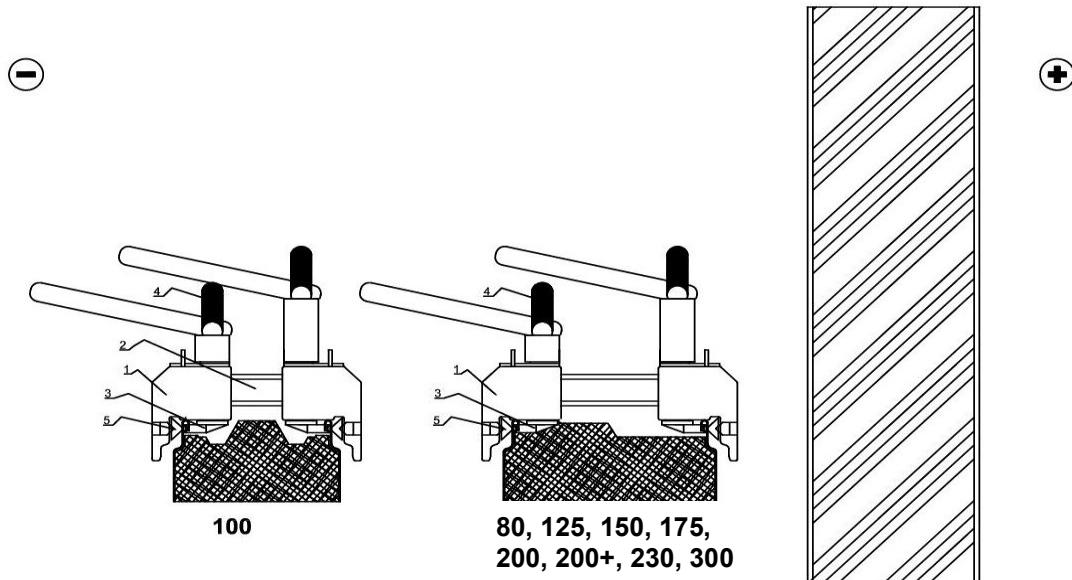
Части подъемника: 1. корпус, 2. фиксатор регулятора ширины корпуса, 3. захватывающая пластина, 4. закрепляющий рычаг и 5. стопорный шип.
